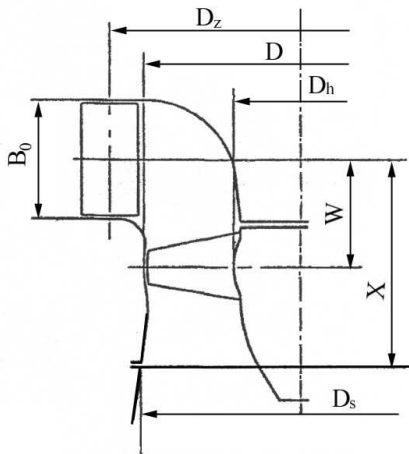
7 Dimensiunile principale ale unui rotor de turbină axială [126]
